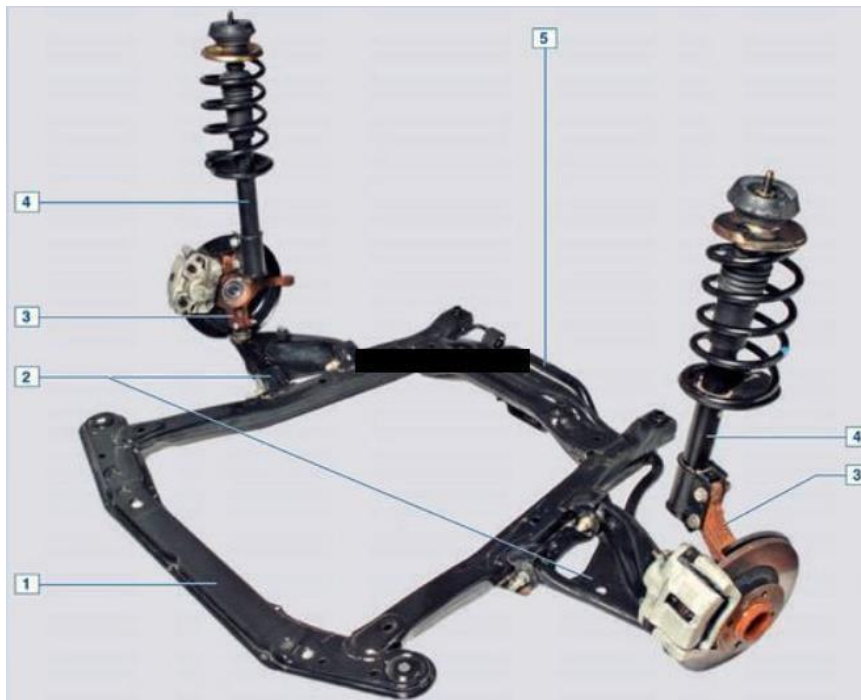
Загальний вигляд пристрою передньої підвіски
